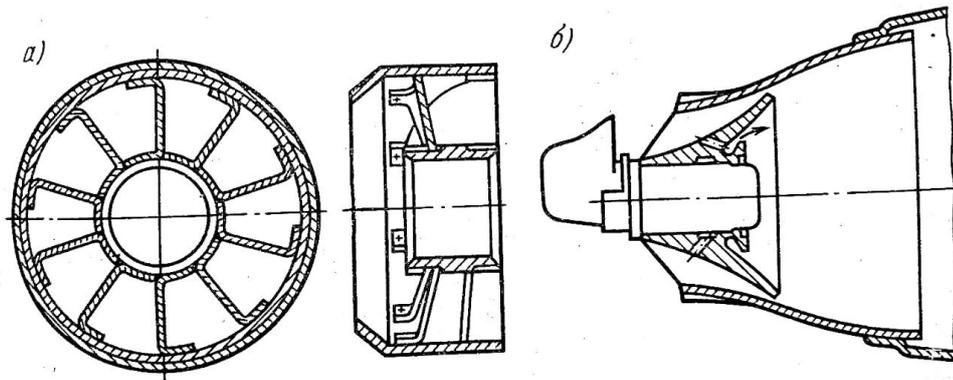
Завихрювачі: а-лопатковий; б-безлопатковий
